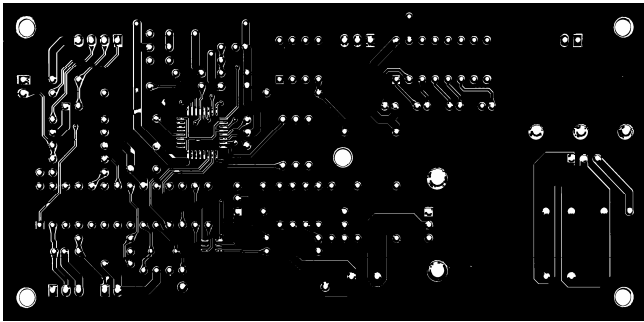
은 검사 대상 PCB 영상의 전처리 과정을 거친 후 모습이다.
